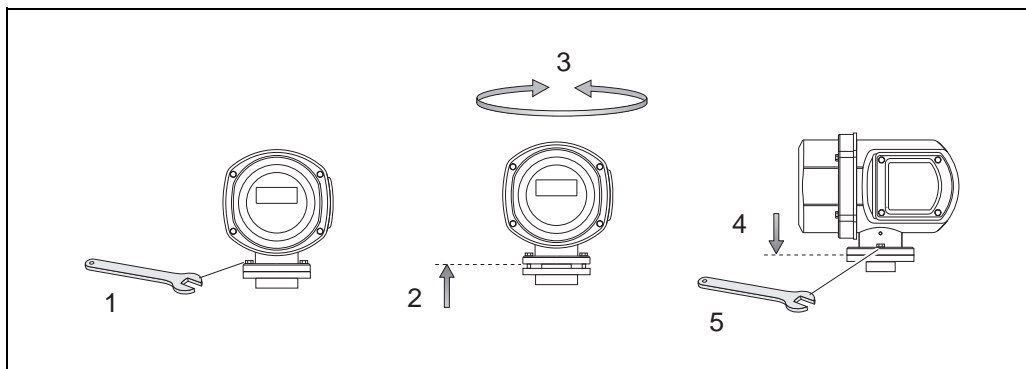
Drehen des Messumformergehäuses (Edelstahl-Feldgehäuse)
